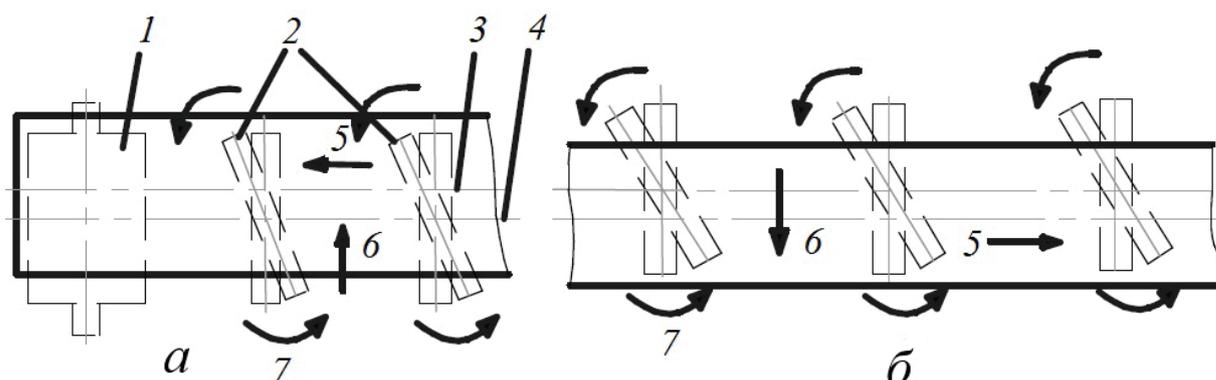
Регулировка верхних роликоопор ленточного конвейера при сходе ленты:
